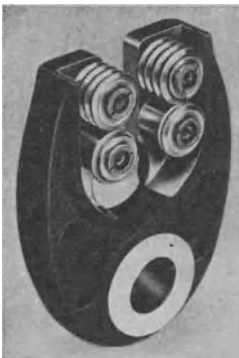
Gewindegrensrachenlehre (Aggra-Lehre). Ausführungsform zum Messen von Gewinden bis an einen Kopf oder Flansch. (Bauer & Schaurte, Hamburg.)
